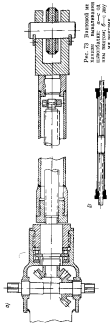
Детали сервошлюпбалки: а — вид сверху; б — вид сбоку
